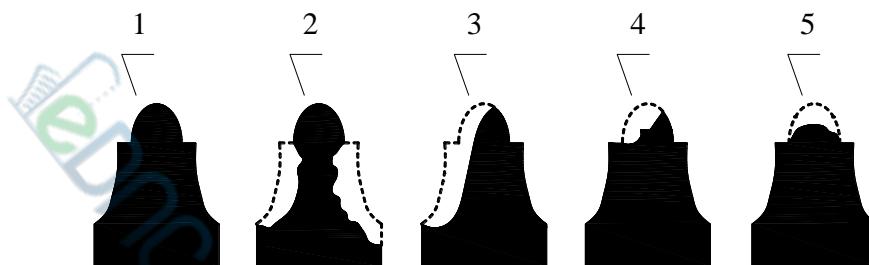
Виды износа и разрушения фрезерных зубьев:
